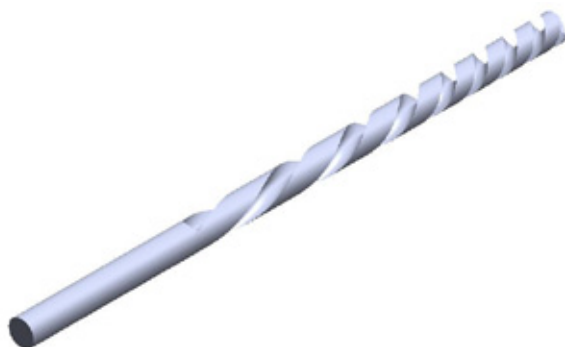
Компьютерная модель сверла с переменным шагом винтовой канавки
